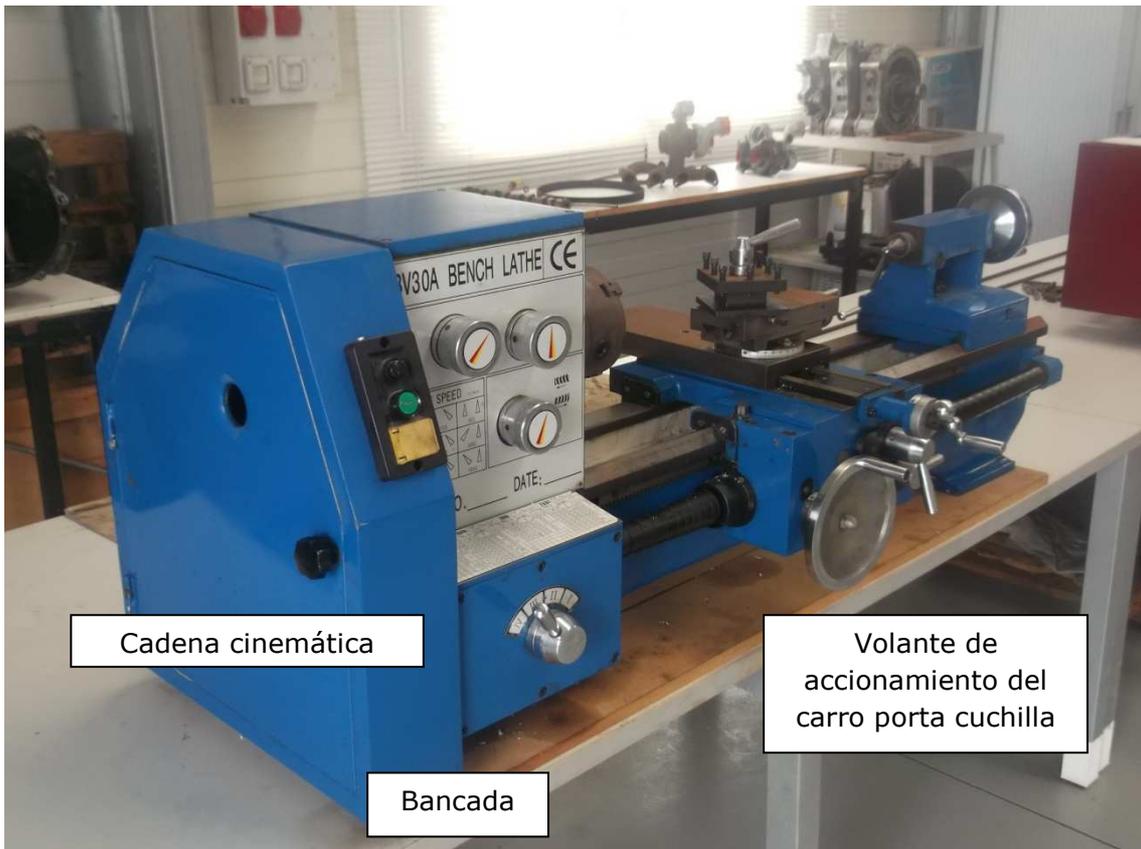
Vista frontal – lateral de la máquina herramienta TORNO. Partes fundamentales.
